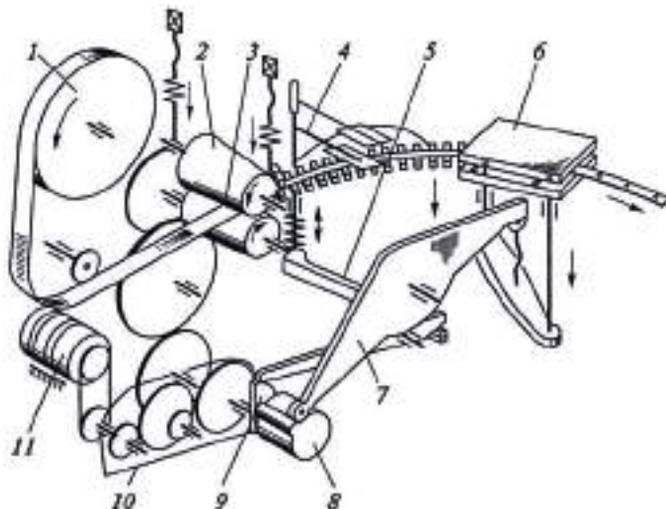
Схема питания автомата ленточным материалом: 1 – барабан; 2, 3 – ролики; 4 – прижимное устройство; 5, 7 – рычаги; 6 – штамп; 8, 9 – кулачки; 10 – редуктор; 11 – электродвигатель
